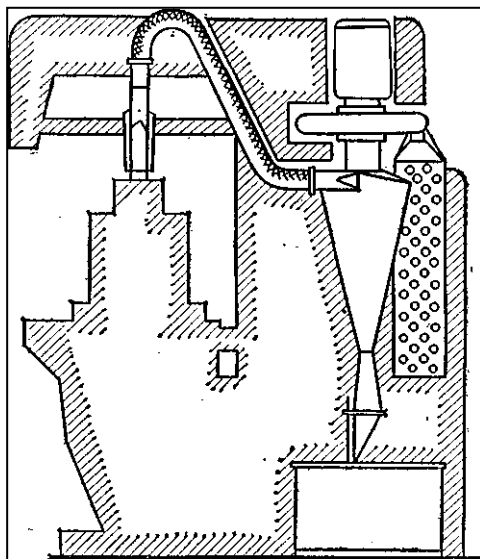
Оборудование фрезерного станка для удаления из зоны резания стружки и пыли
